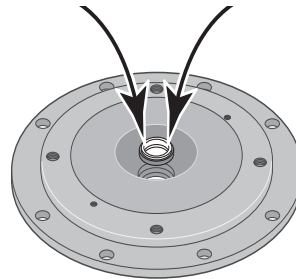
POUSSER LE NOUVEAU JOINT EN PLACE
